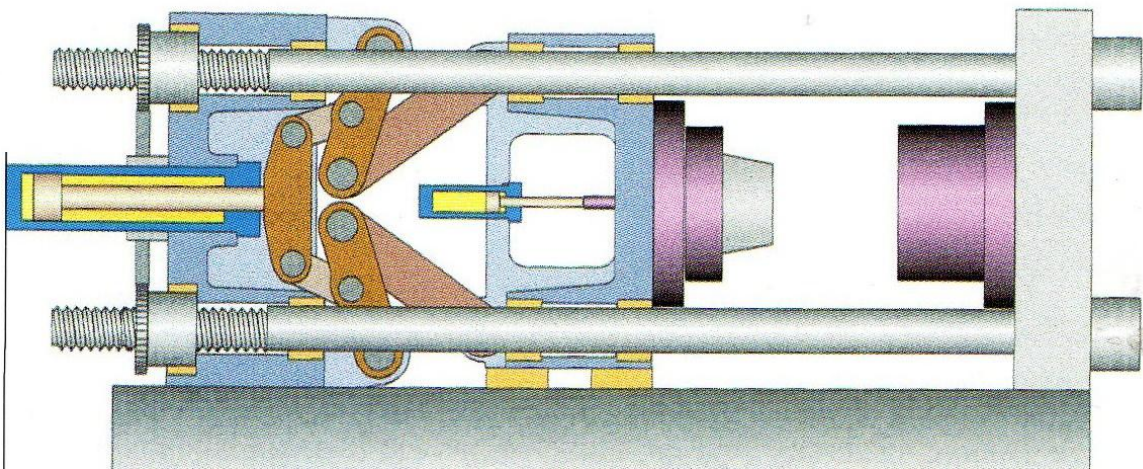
Partes principales de la unidad de cierre antes señalados de una maquina con un sistema de cierre de doble rollidera.
